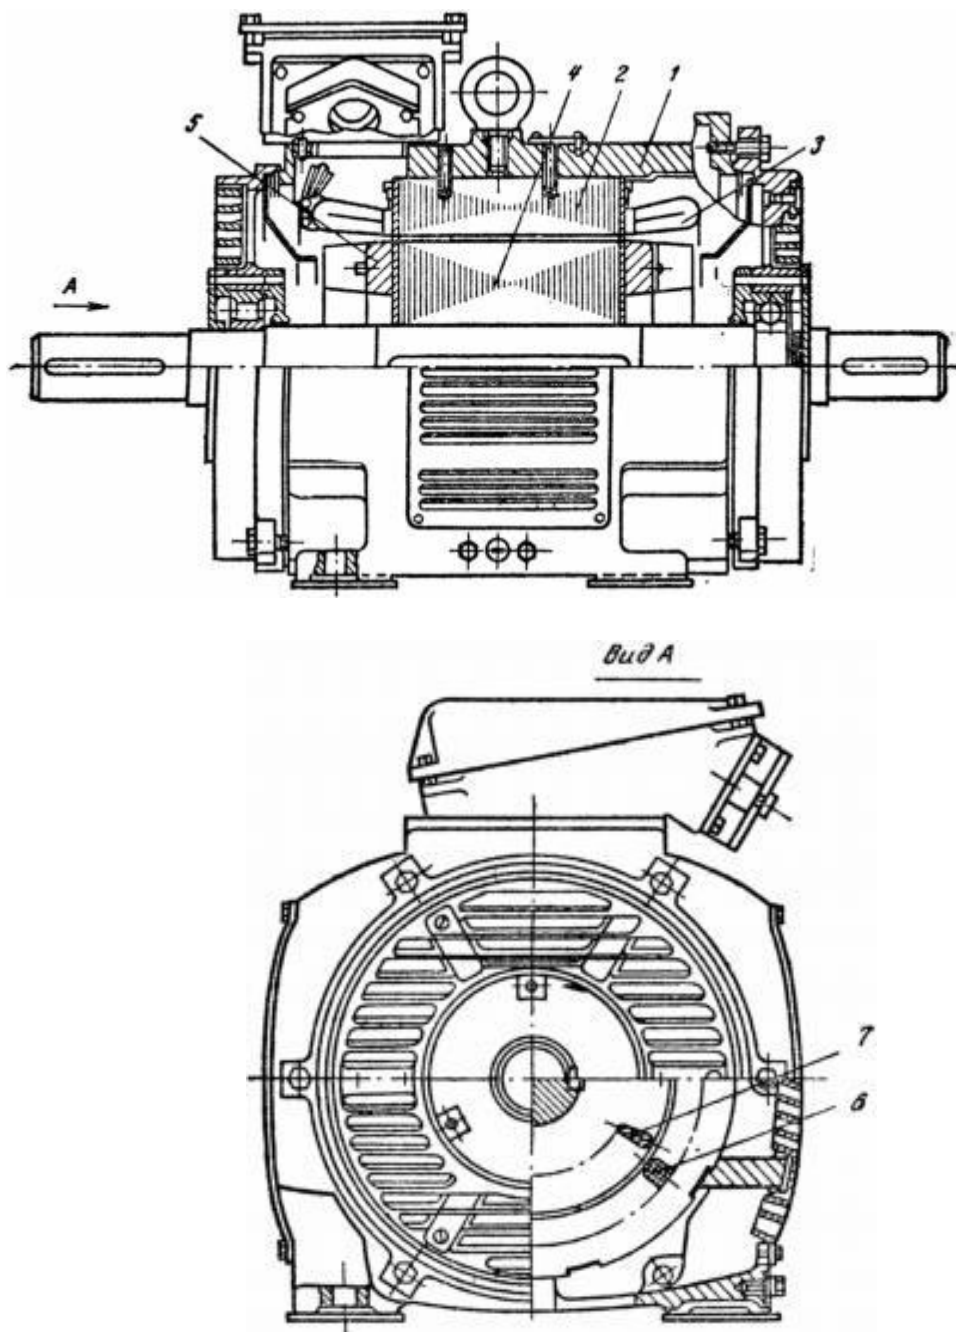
АД серии 4А со степенью защиты IP44 короткозамкнутым ротором закрытого обдуваемого исполнения: 1- станина; 2- сердечник статора; 3- обмотка статора; 4- сердечник ротора; 5 - короткозамыкающие кольца; 6- паз статора; 7- паз ротора
